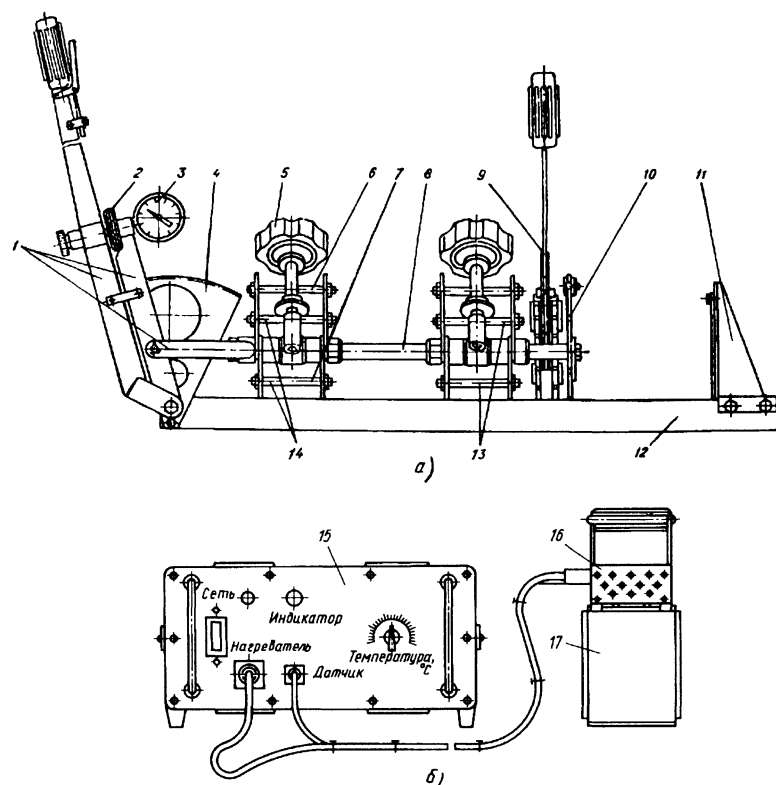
Установка для стыковой сварки пластмассовых труб диаметром 63...110 мм нагретым инструментом:
